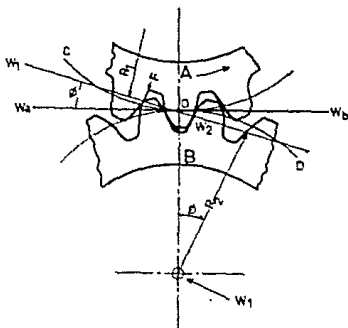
Fuerzas que actúan en los dientes de engranes
